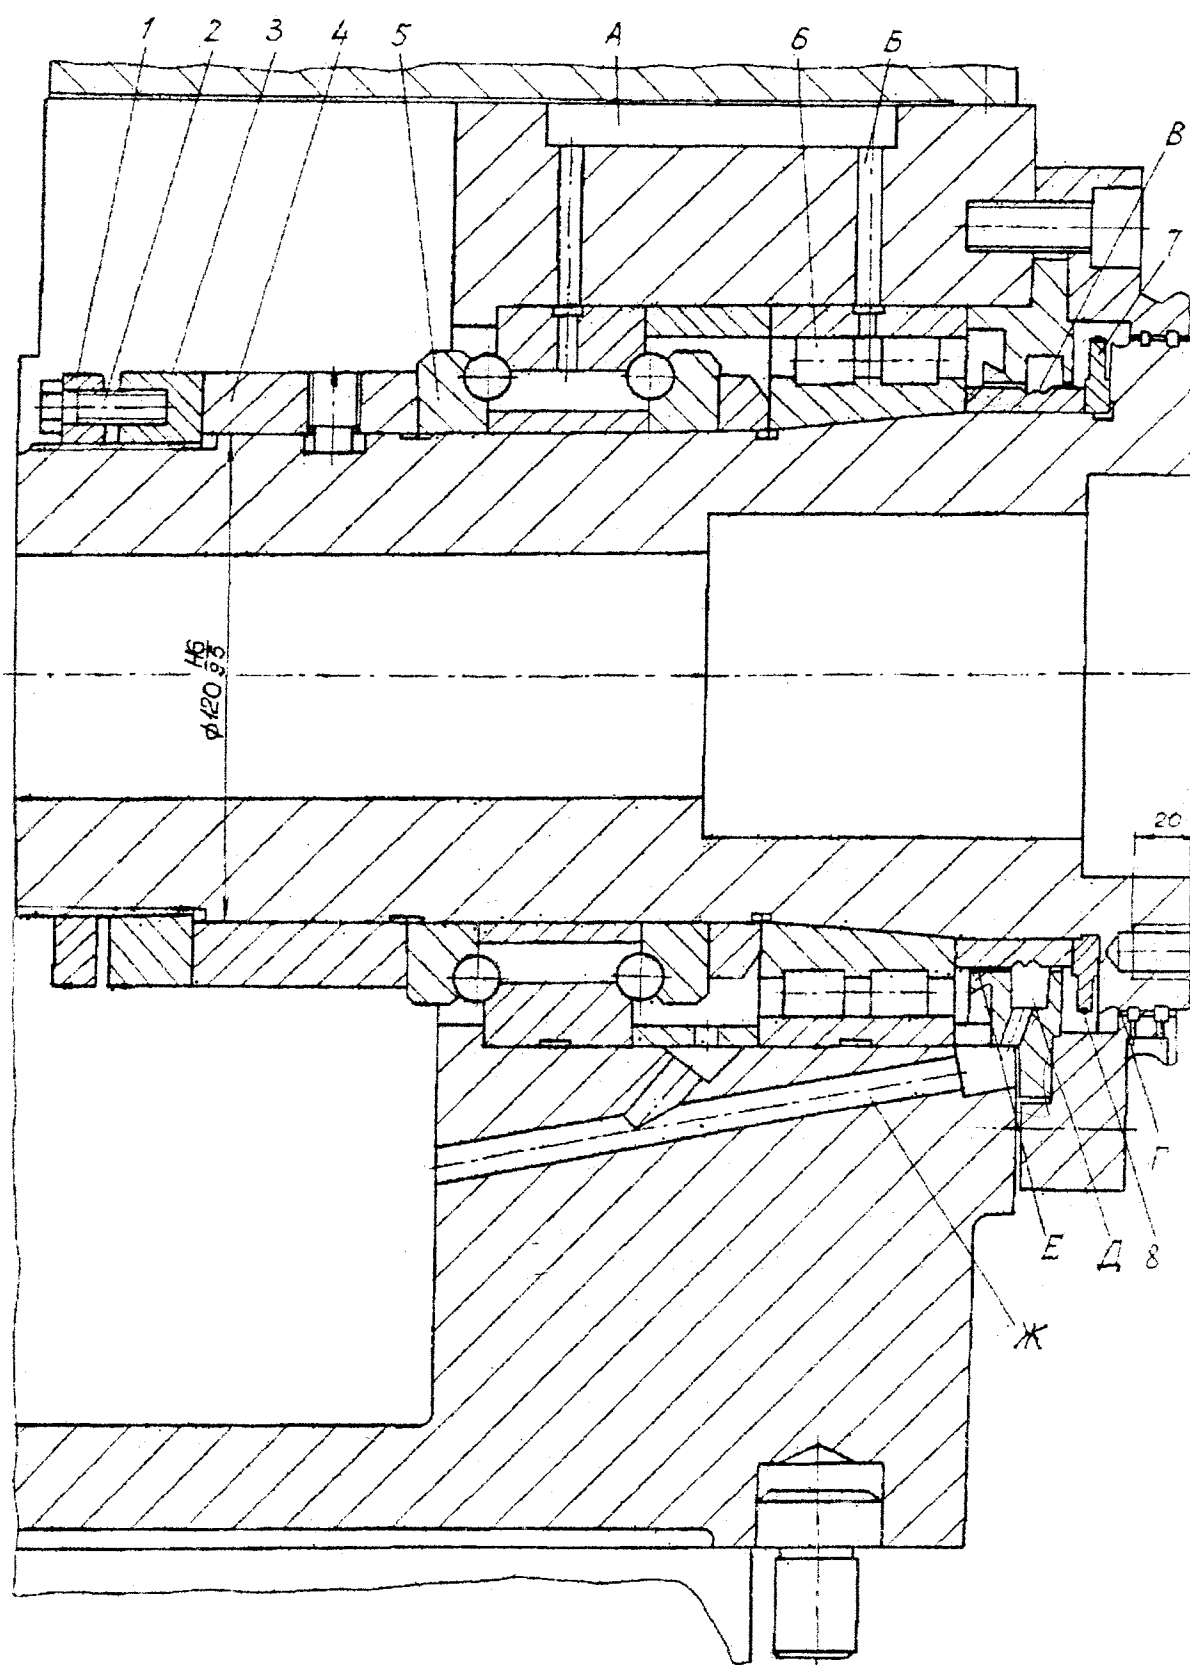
Передняя опора и конец шпинделя многоцелевого фрезерно-сверлильно-расточного станка
